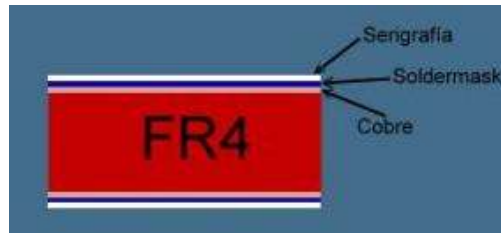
CORTE TRANSVERSAL DE UNA PCB
